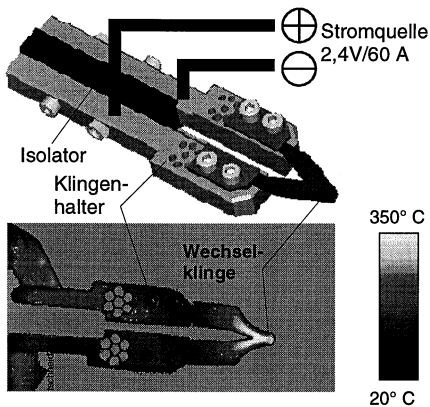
Aufbau und Wärmebild eines thermischen Schneidwerkzeugs
